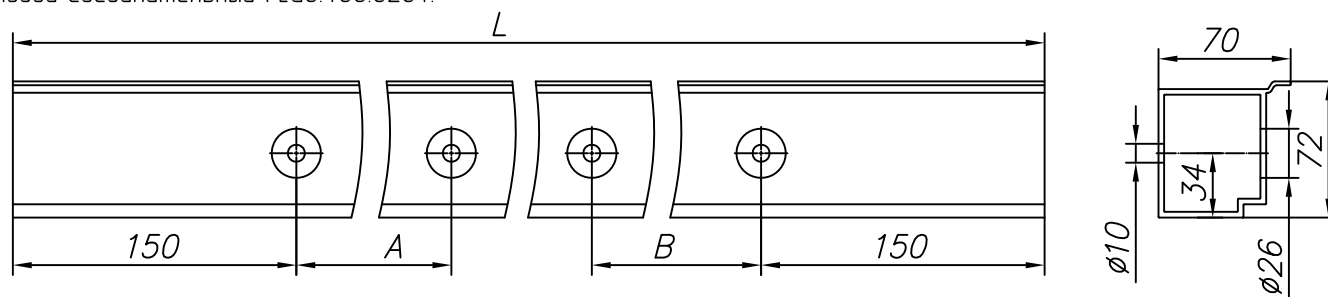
Изготовление столба FLGU.400.0502
